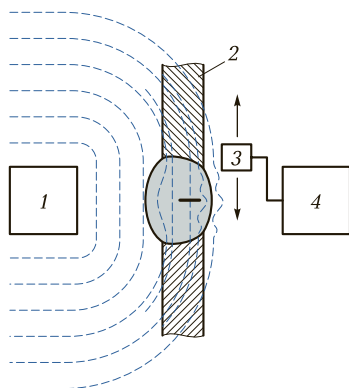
Схема контроля сварного соединения методом вихретоковой дефектоскопии (стрелками показаны направления перемещения датчика):
